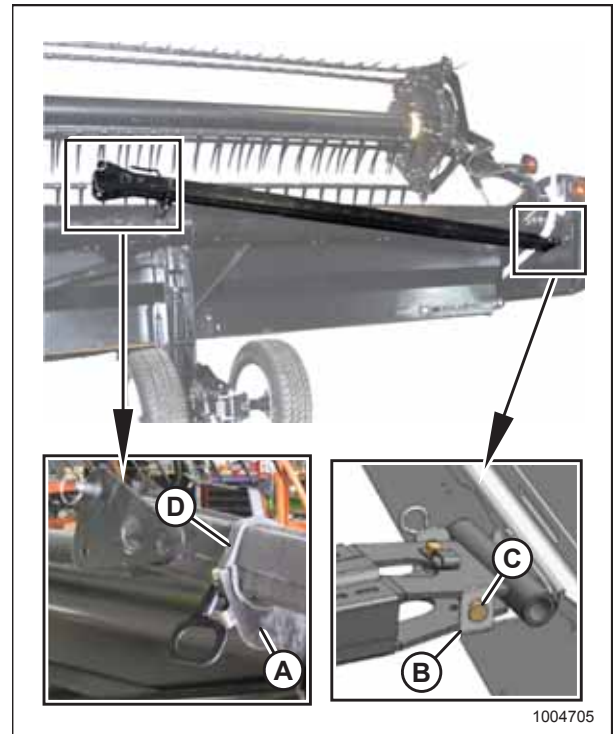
Extracción de la barra de remolque - Lado derecho
